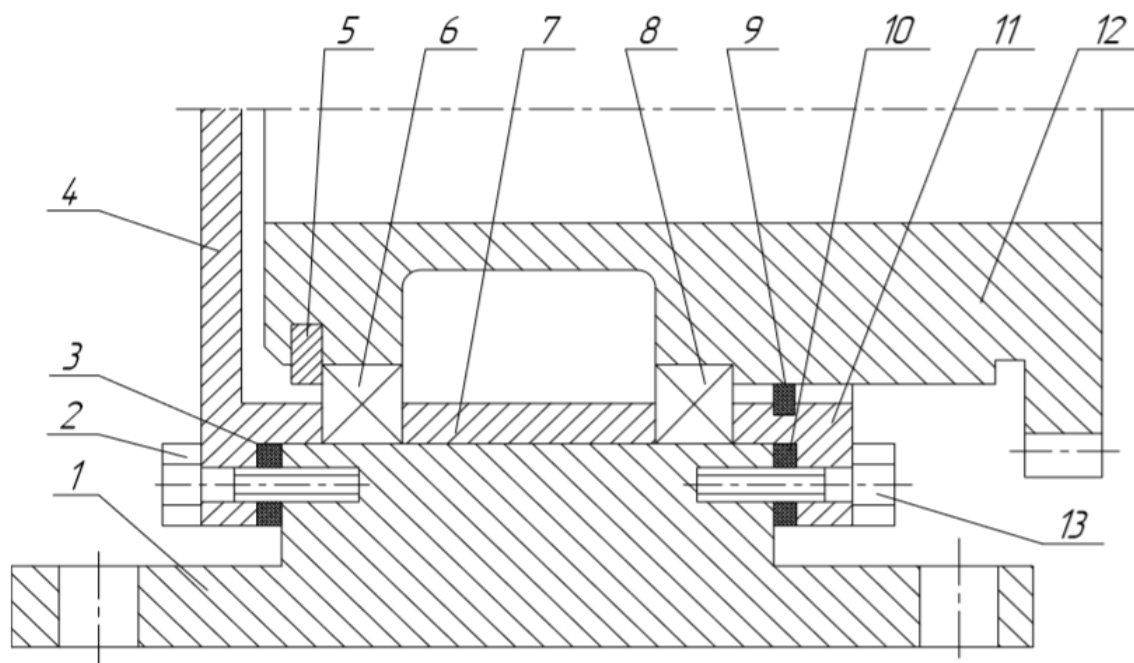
Эскиз узла в сборе: 1 – корпус; 2 – винт; 3 – прокладка; 4 – крышка; 5 – шайба; 6 – подшипник; 7 – втулка; 8 – подшипник; 9 – кольцо; 10 – прокладка; 11 – крышка; 12 – вал; 13 – винт
